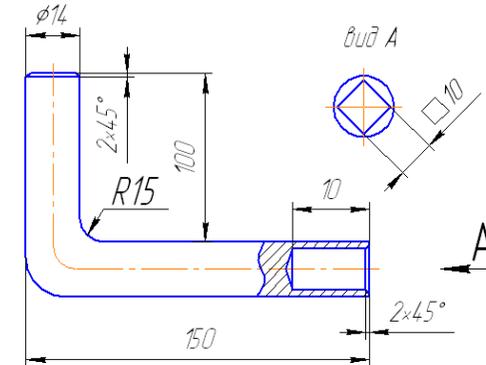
Ключ для выворачивания гнезда предохранительного клапана
